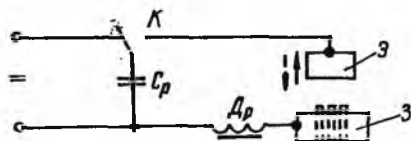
Принципиальная схема дуговой конденсаторной сварки «оплавлением в шарик».
